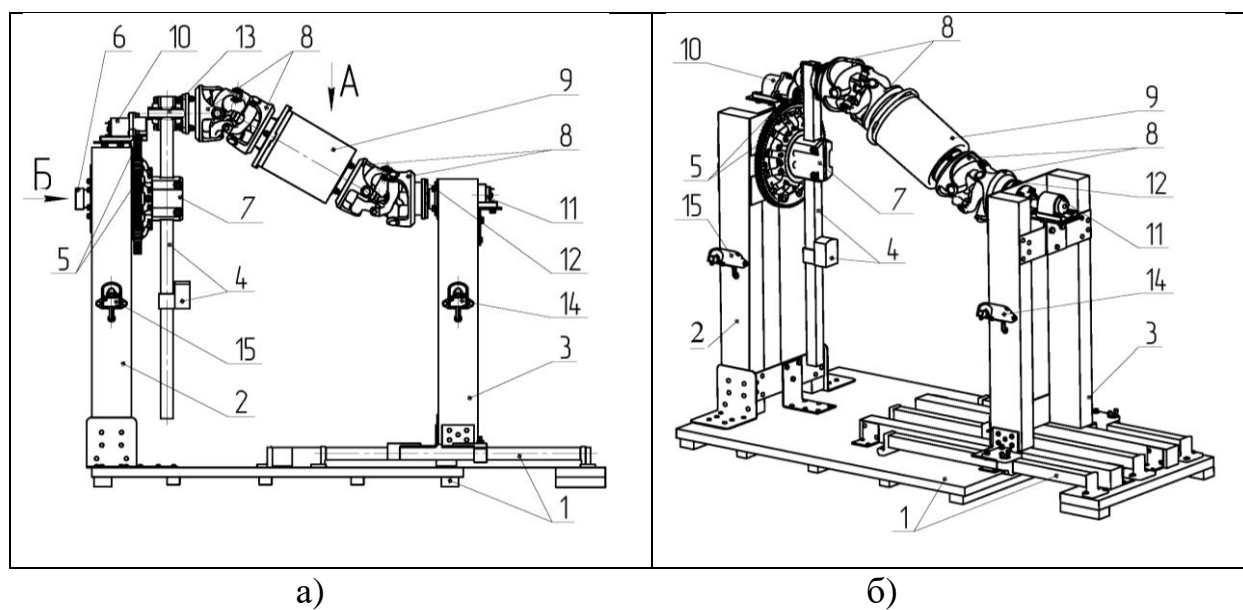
Вид загальний експериментальної машини для обробки деталей («а» - вид спереду, «б» - наочне зображення)
